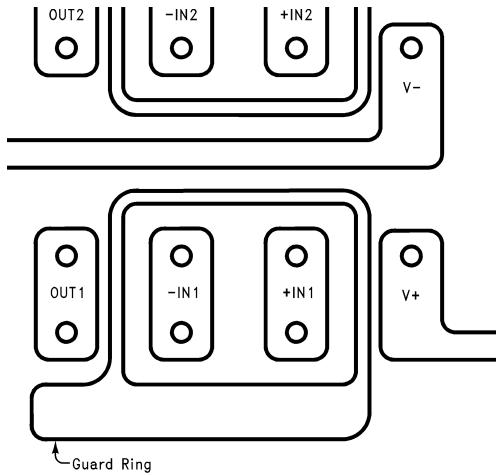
PCB レイアウトでのガード リングの代表的な接続例
